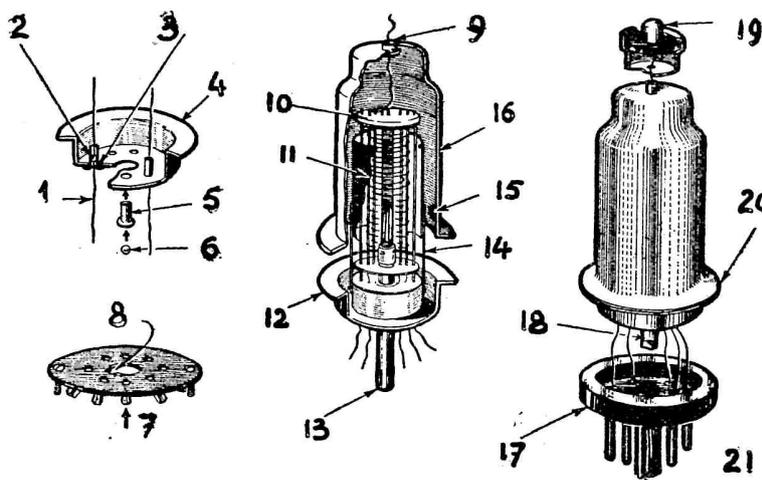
a). — Détail du montage d'un "Métal-Tube" : 1. — Fil de connexion ; 2. — Perle de verre soudée dans l'œillet en fer-nico ; 3. — Soudure de l'œillet de fer-nico sur le socle en acier ; 4. — Socle en acier ; 5. — Œillet de fer-nico ; 6. — Perle de verre ; 7. — Support standard pour culot "Octal" ; 8. — Logement de l'ergot du tétén ; 9. — Perle de verre, œillet de fer-nico pour passage de la connexion de grille ; 10. — Pont mica ; 11. — Electrodes ; 12. — Socle en acier ; 13. — Tube d'évacuation des gaz ; 14. — Support de la plaque en mica ; 15. — Pastille de magnésium "getter" ; 16. — Enveloppe en acier ; 17. — Culot en bakélite ; 18. — Soudure du tube d'évacuation des gaz ; 19. — Chapeau de grille ; 20. — Soudure électrique entre le socle et l'enveloppe en acier ; 21. — Tétén en bakélite avec son ergot
